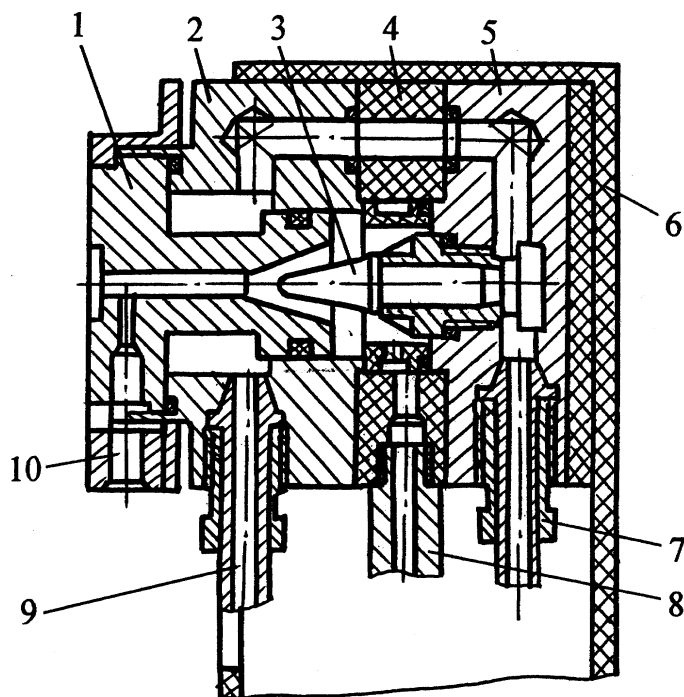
Плазмовий розпилювач ПП-25: 1 – анод-сопло; 2 – корпус анодного вузла; 3 – катод; 4 – ізолятор; 5 – корпус катодного вузла; 6 – рукоятка; 7 – штуцер для подавання води охолодження; 8 – штуцер для подавання газу; 9 – штуцер для відведення води; 10 – отвір для штуцера, по якому подається порошок або дріт
